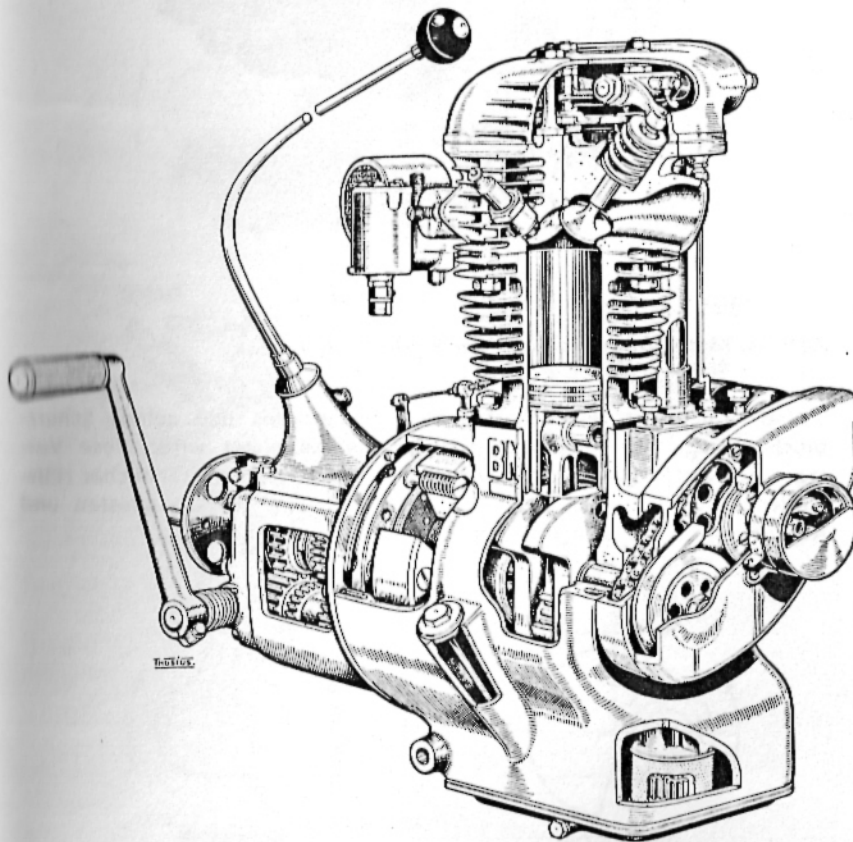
Motor-Getriebeblock der R 4-Maschine
